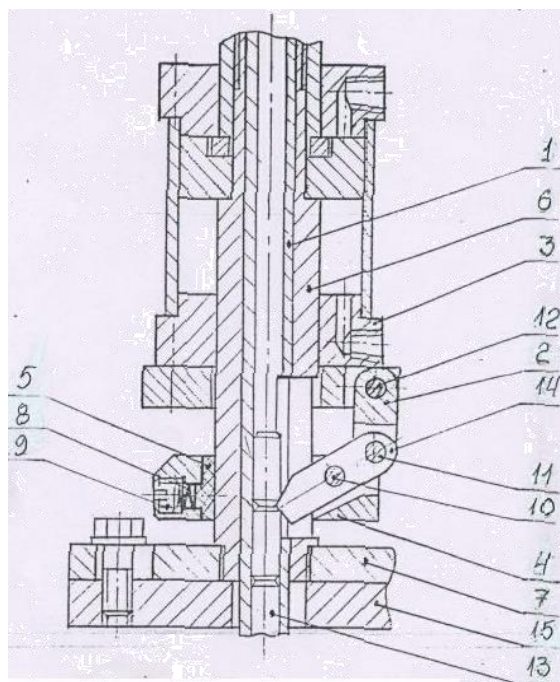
Эскиз устройства для загрузки заготовок.
